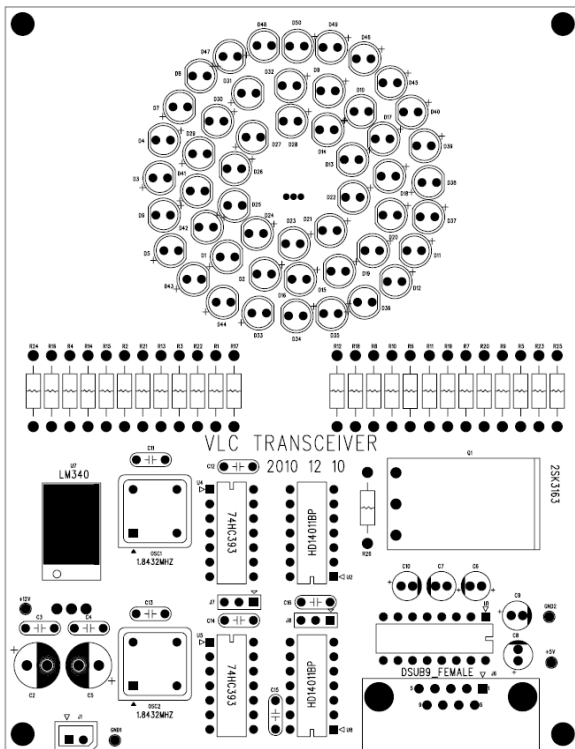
RS-232C 가시광 송신회로의 PCB 도면.
